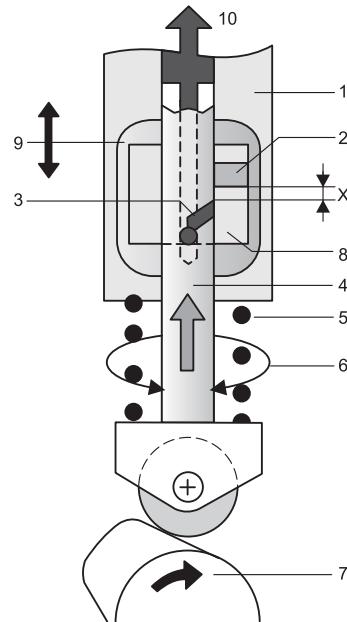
Система впрыска с рядным ТНВД с дополнительной втулкой: 1 — гильза плунжера; 2 — выпускное окно; 3 — регулирующая кромка плунжера; 4 — плунжер; 5 — возвратная пружина плунжера; 6 — поворот плунжера регулирующей рейкой; 7 — кулачковый вал; 8 — дополнительная втулка; 9 — изменение хода плунжера за счет регулирующей втулки; 10 — подача топлива к форсунке; X — активный ход плунжера
